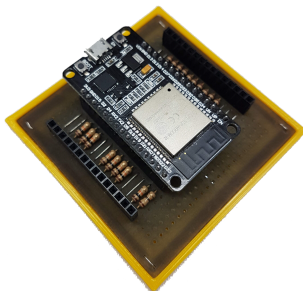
Placa perfurada montada com todos os resistores soldados.
